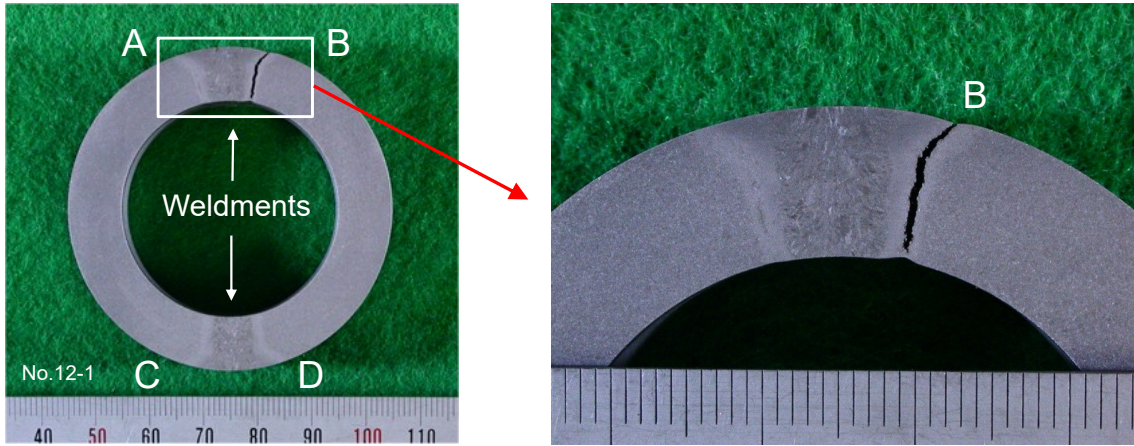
内圧クリープ試験体の破壊後の断面状況 (No. 12-1)
